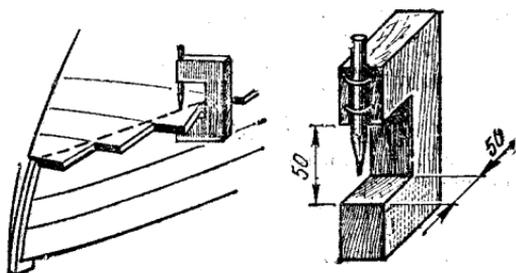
Приспособление для причерчивания торцов досок днищевой обшивки.
